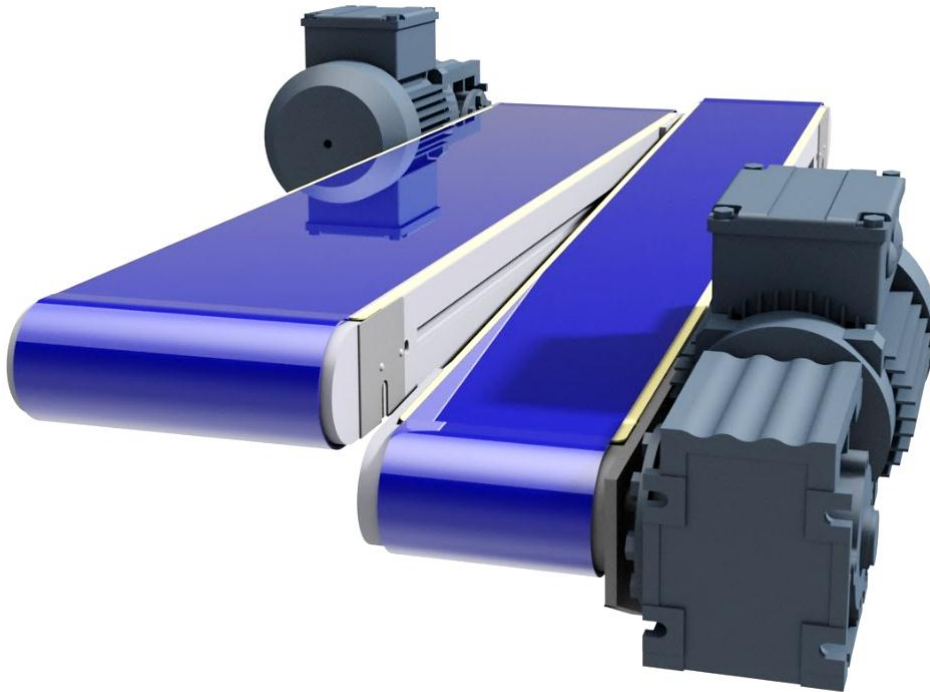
Dopravník GUF-P 2000 šířky pásu 150 mm s motorem od firmy MK-Technology [12]
